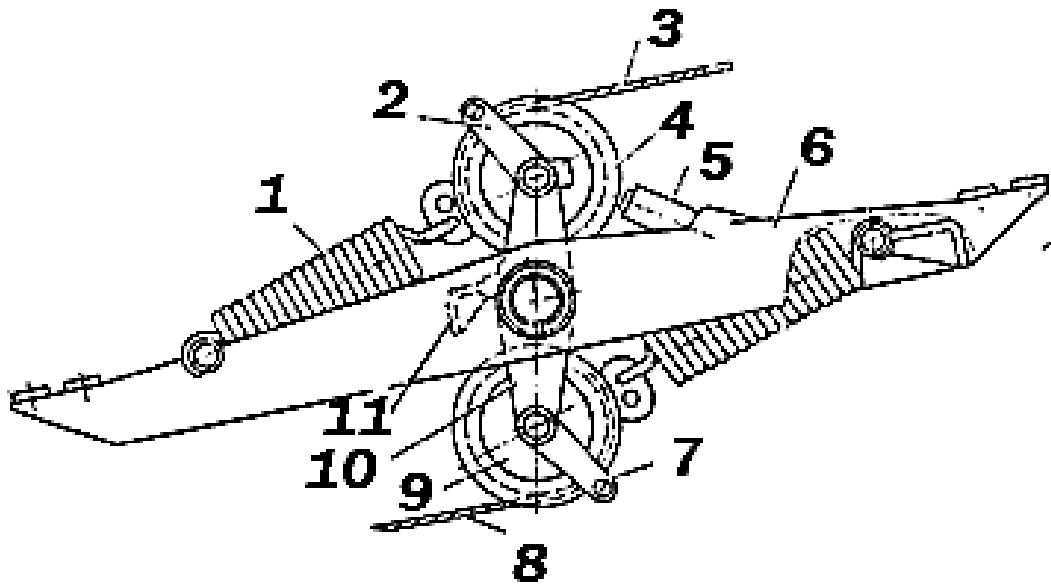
Регулятор натягу тросів: 1 – пружина; 2, 7 – обмежники тросів; 3,8 – троси; 4,9 – ролики; 5,11 – упори; 6 – корпус; 10 – качалка
